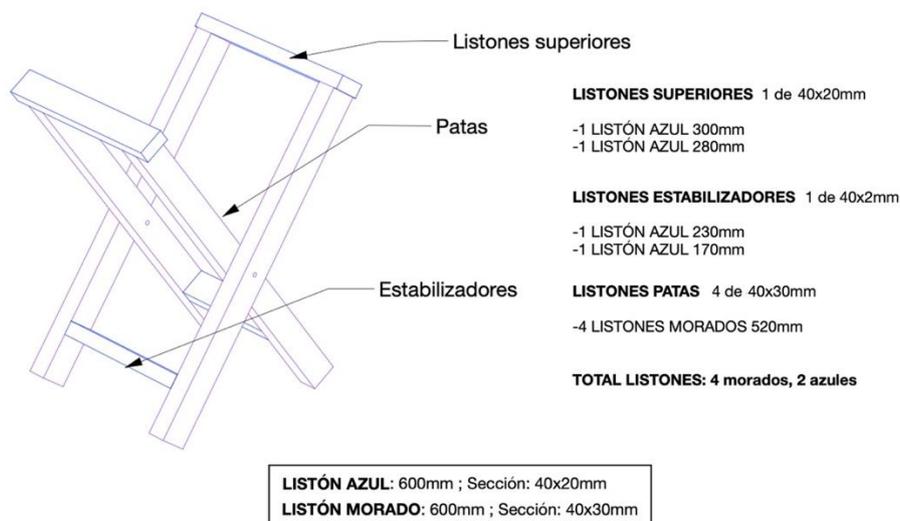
ESQUEMA PARA MONTAJE DE TABURETE PLEGABLE. FUENTE: PROPIA
